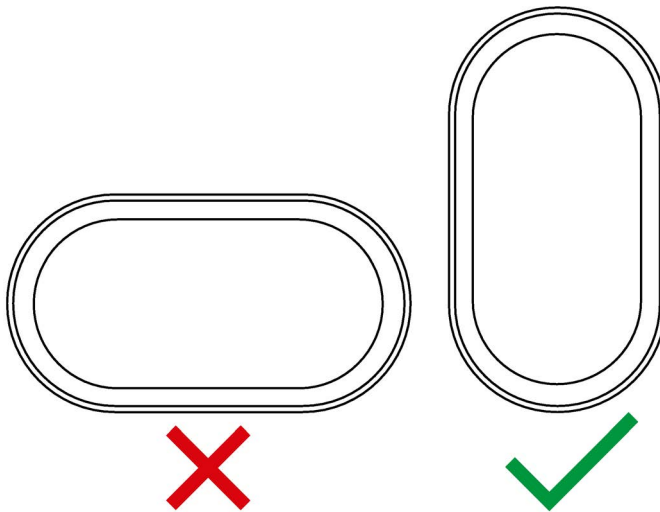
Posición de montaje de la caperuza protectora para pulsador doble
